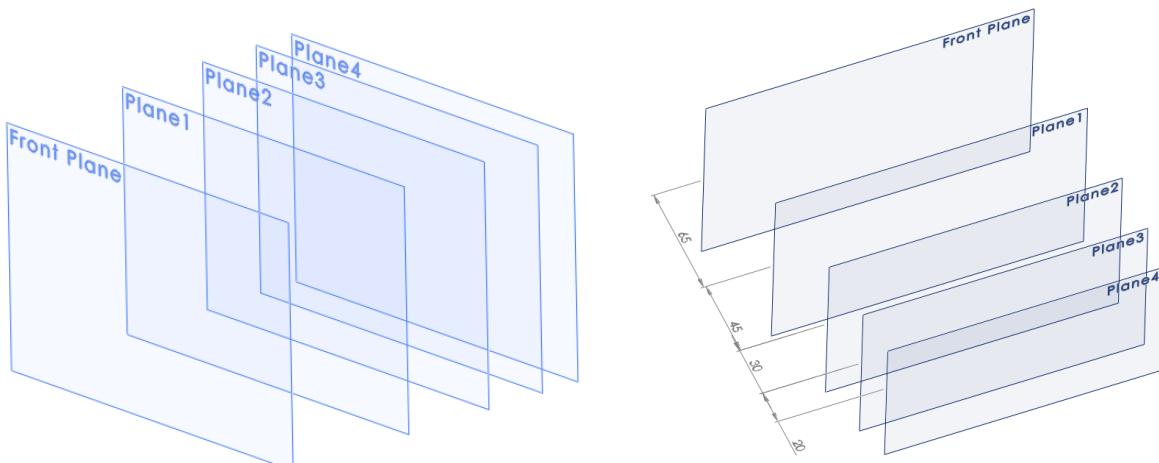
3 Stabilirea planelor și a distanțelor dintre acestea
